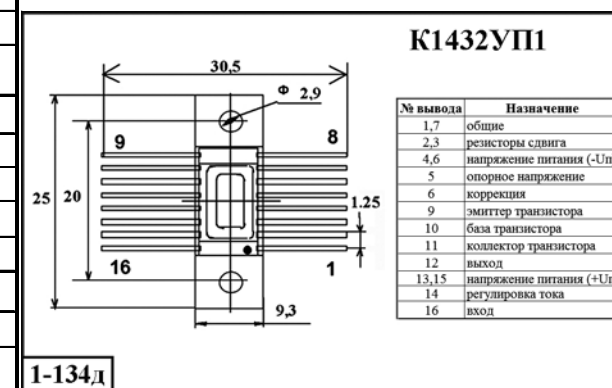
д. Внешний вид и габаритные размеры микросхемы К1432.
